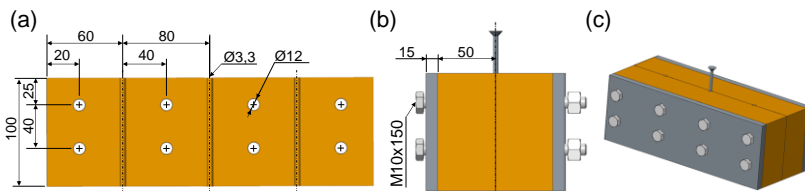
Prüfkörper für die Analysetechnik *Sectional Imaging*: Eine Hälfte des Prüfkörpers (a), beide Hälften mit Halterung und Holzschraube in der Vorderansicht (b) sowie 3D-Ansicht des Aufbaus mit Holzschraube an der mittleren der drei möglichen Prüfpositionen (c). (Hölz, Grauburger & Matthiesen, 2020a)
